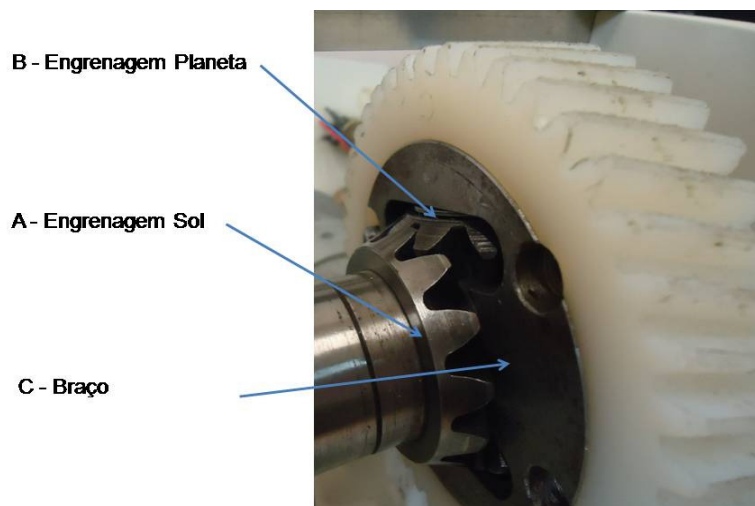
Identificação dos elementos que caracterizam a engrenagem planetária.
